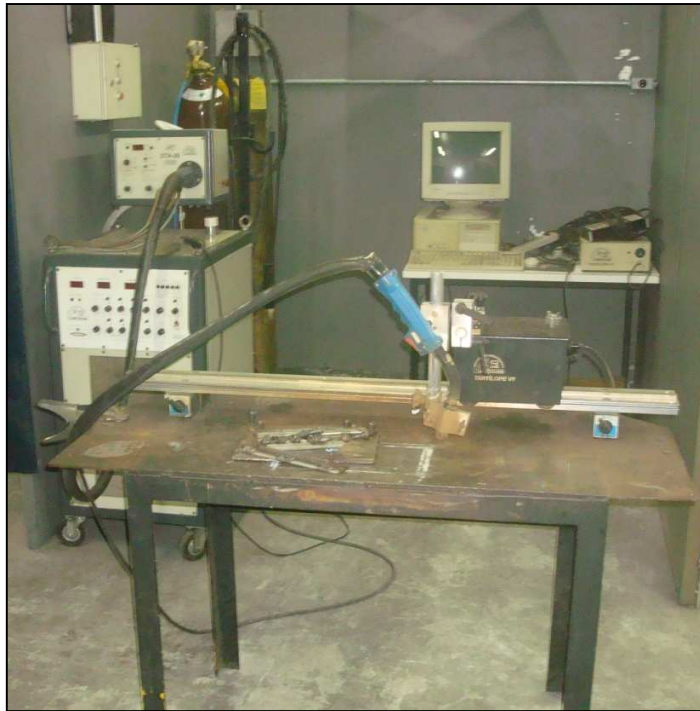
Equipamento de soldagem com arame tubular utilizado para os ensaios
